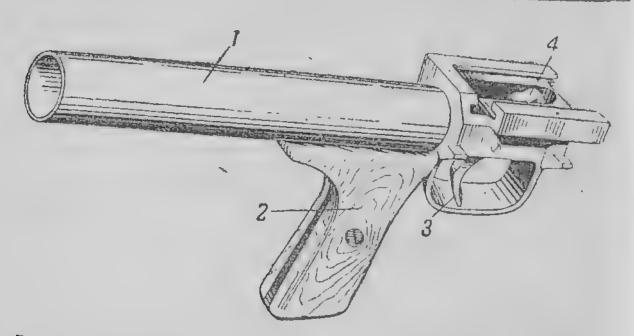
Спусковая коробка с внутренней трубой: 1—внутренияя труба; 2—рукоятка; 3—спусковой крючок; 4—шептало
